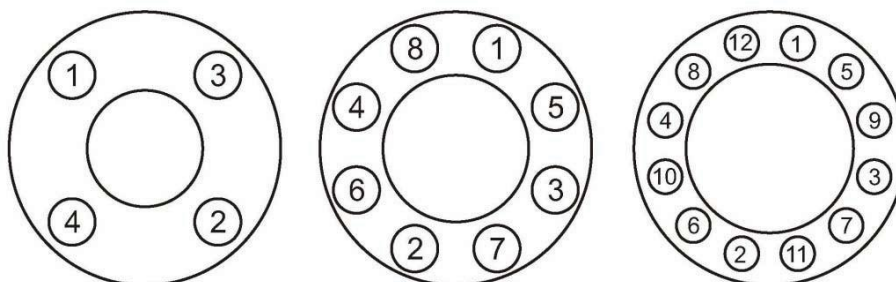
Порядок затяжки гаек на фланцах
